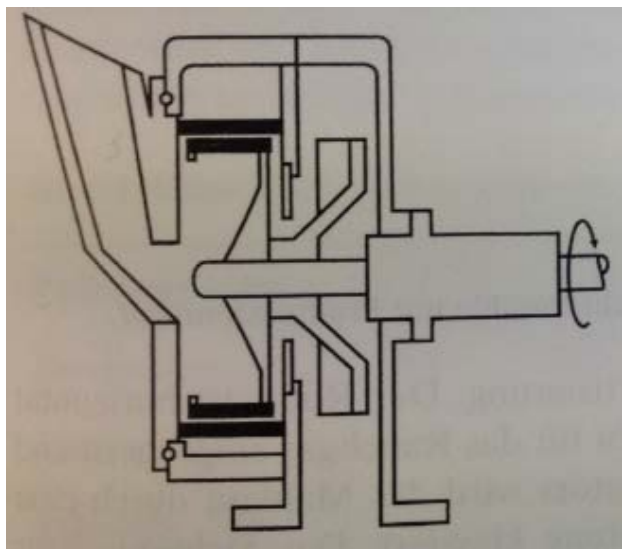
Mühle mit Prallplattenrotor und Stromklassierung (42)
